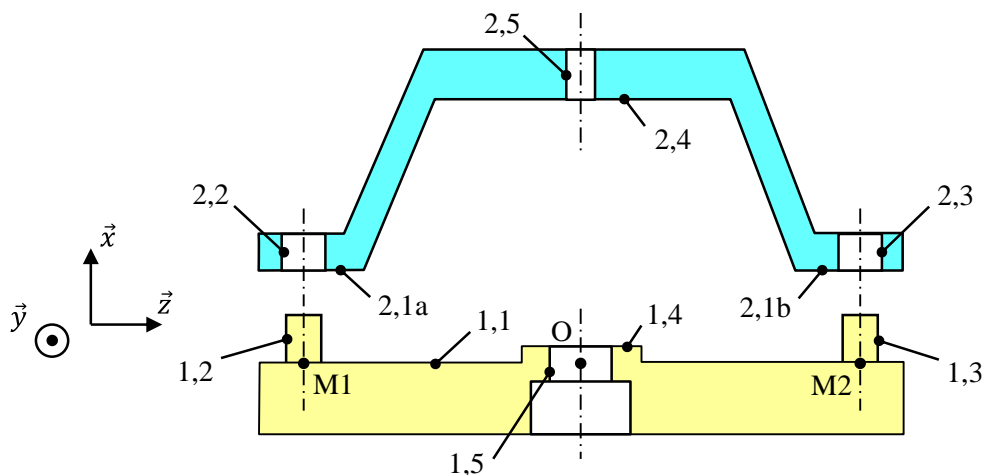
Surfaces de contact entre les deux pièces de l'assemblage étudié
